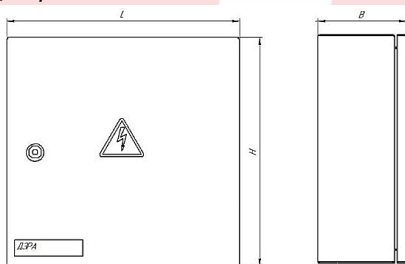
Общий вид и габаритные размеры УОЩ, УОЩВ
